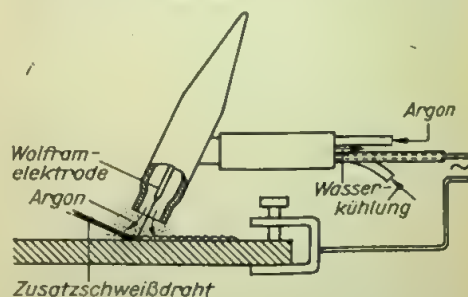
Wolfram-Inertgas-(WIG-)Schweißen
